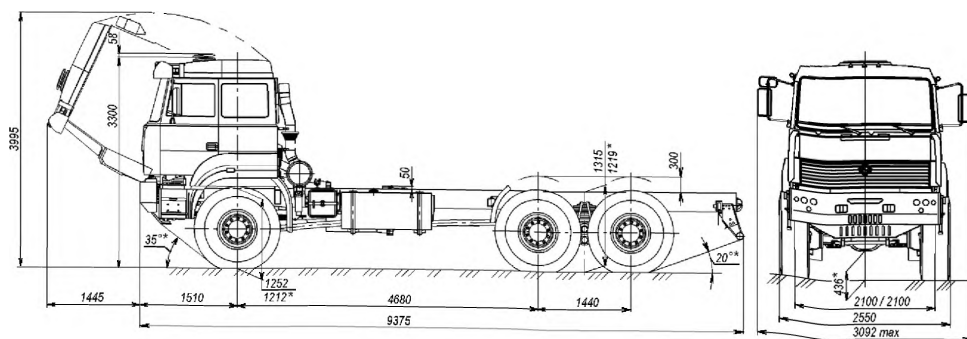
Размеры габаритные шасси Урал-63701-1951
